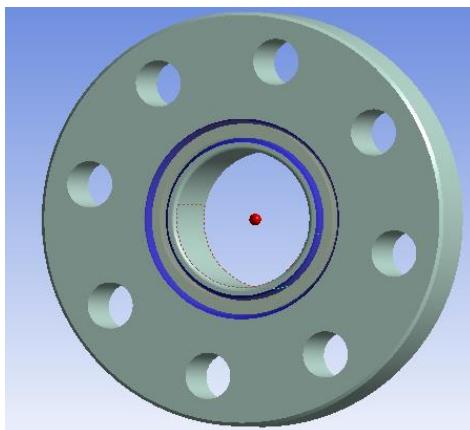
Definição das superfícies de contato entre o flange e o anel (Autores)
